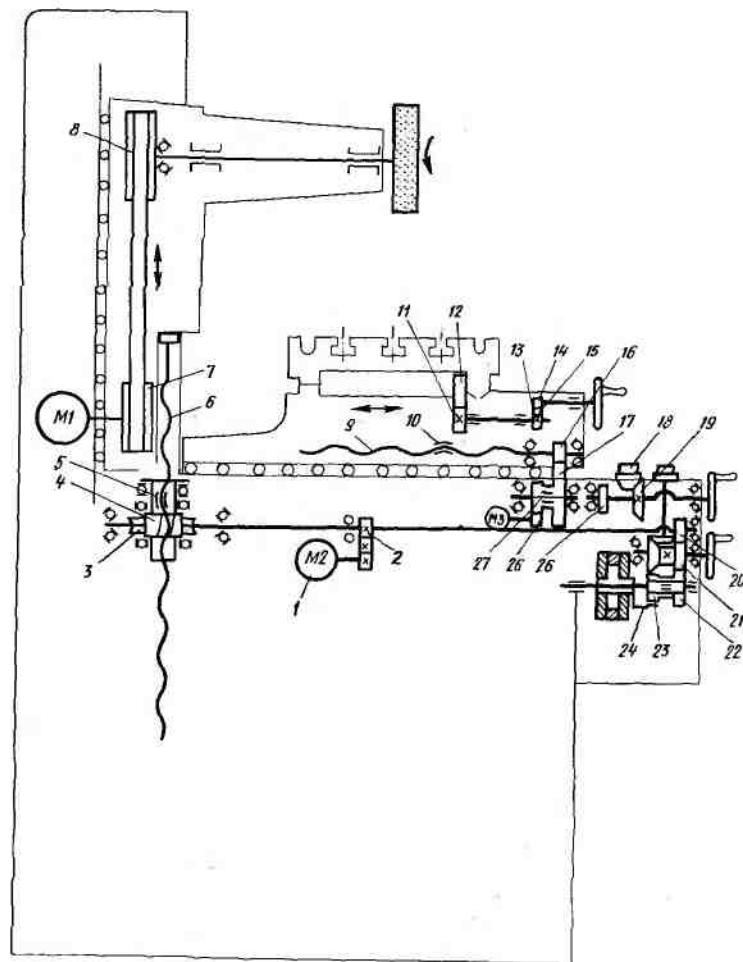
Кинематическая схема универсального плоскошлифовального станка мод. 3Г714 с горизонтальным шпинделем
